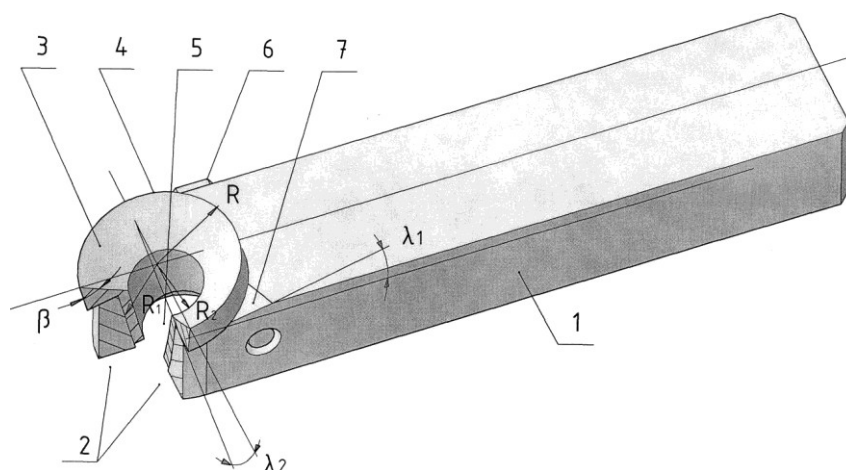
Резец с радиусной режущей кромкой: 1 – стальной корпус резца; 2 – головка; 3 – хвостовик режущего элемента; 4 – торцевая режущая кромкой радиусом R ; 5 – сквозное отверстие радиусом R_2 для удаления стружки; 6 – стопорный болт; 7 – отверстие радиусом R_1 в головке резца перпендикулярно плоскости, которая наклонена вдоль корпуса резца под углом λ_1 относительно горизонтальной плоскости и одновременно под углом λ_2 в вертикальной плоскости
